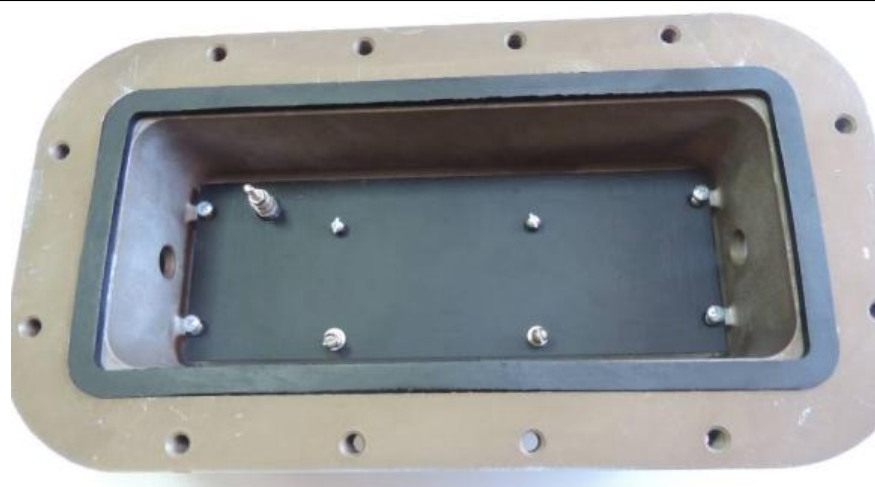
Корпус ККВ-ПА со снятой крышкой. На дне расположена пластина для монтажа РМ-1К-Р3
